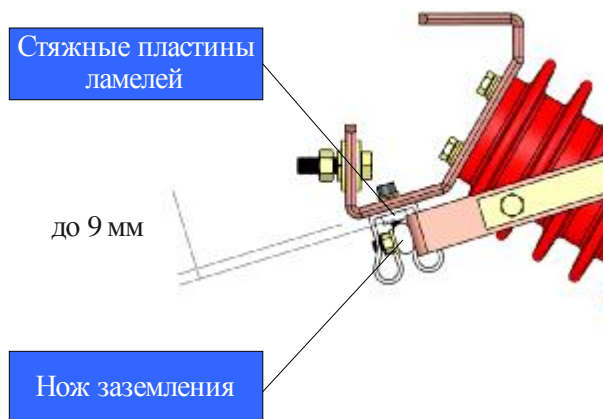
б. Регулировка тяги заземляющего разъединителя.
